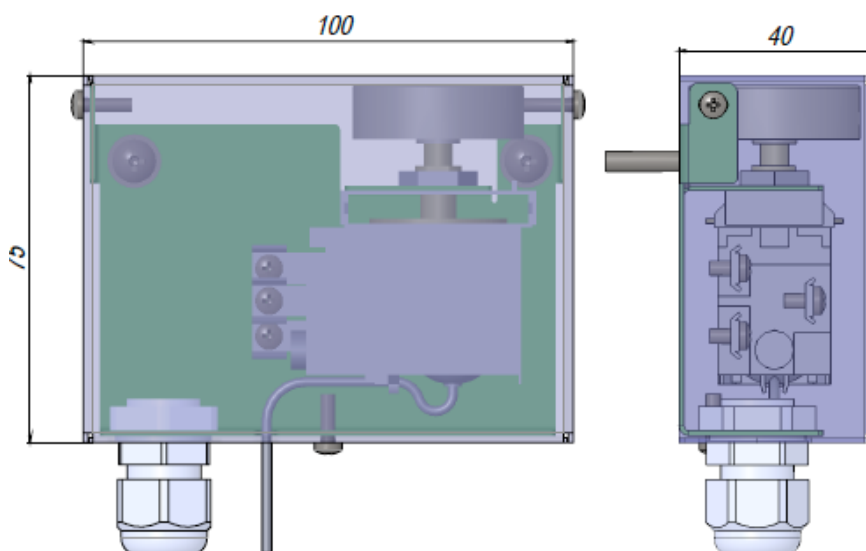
Габаритные присоединительные размеры корпуса реле температуры.
